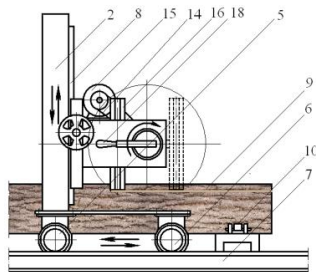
Общий вид ленточнопильного станка (вид сбоку рабочее положение)
